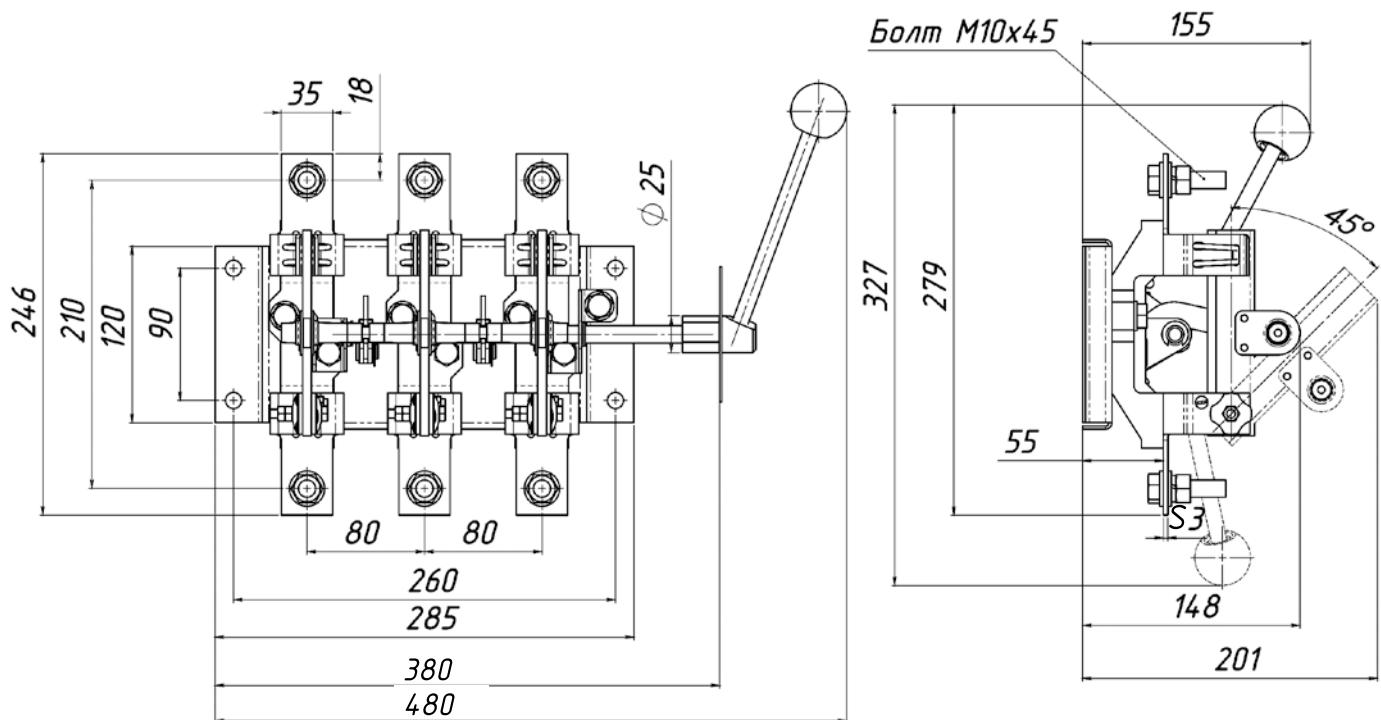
Разъединитель серии Р с боковой рукояткой РБ-6,
